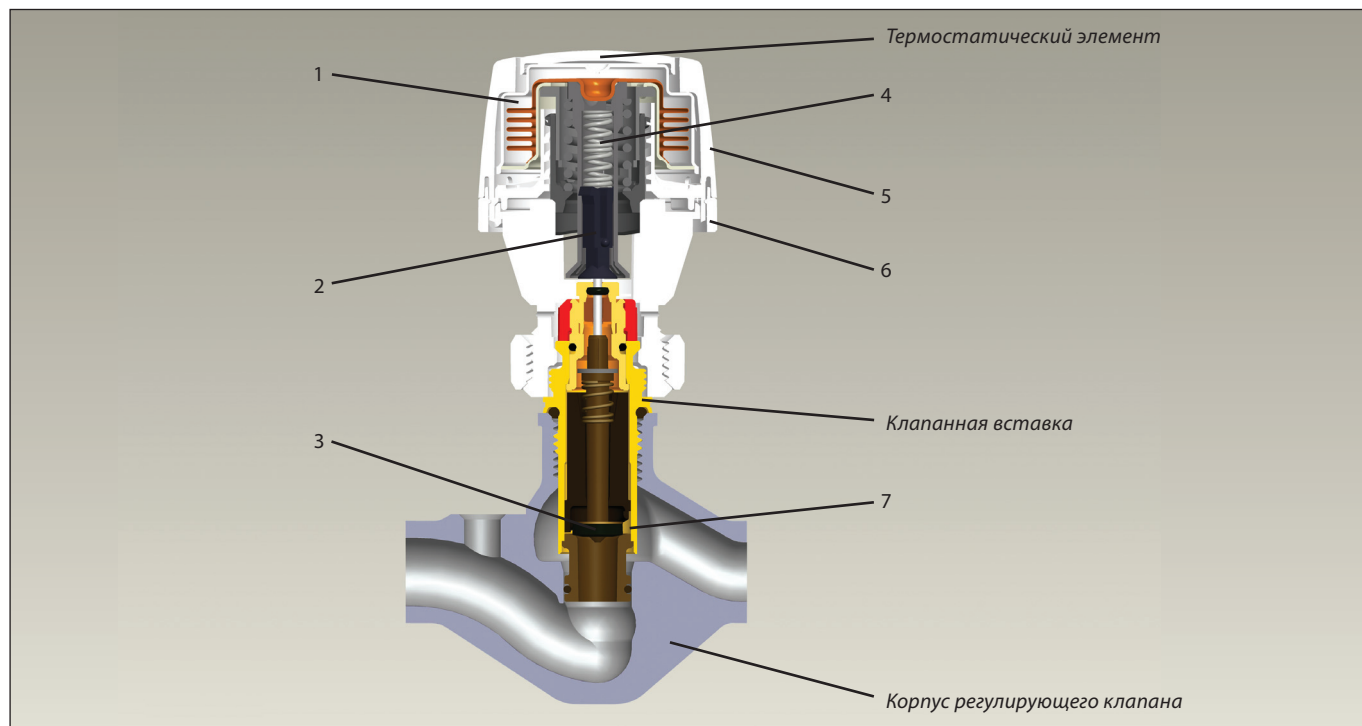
Автоматический радиаторный терморегулятор (для двухтрубной системы отопления). 1 – сильфон; 2 – шток; 3 – золотник; 4 – рабочая пружина; 5 – настроечная рукоятка; 6 – шкала настройки; 7 – дросселирующий цилиндр.
